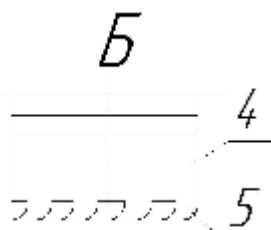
Вид сбоку зубчатой коронки 4 по направлению Б
